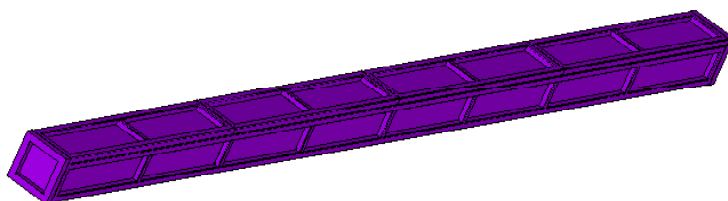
Сварной корпус контейнера для проведения виброударного упрочнения поверхностного слоя обрабатываемого изделия
